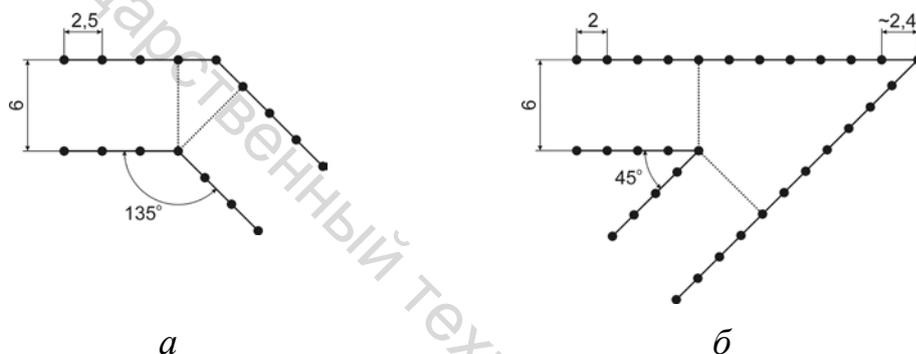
Изготовление угловых двухлинейных строчек:
